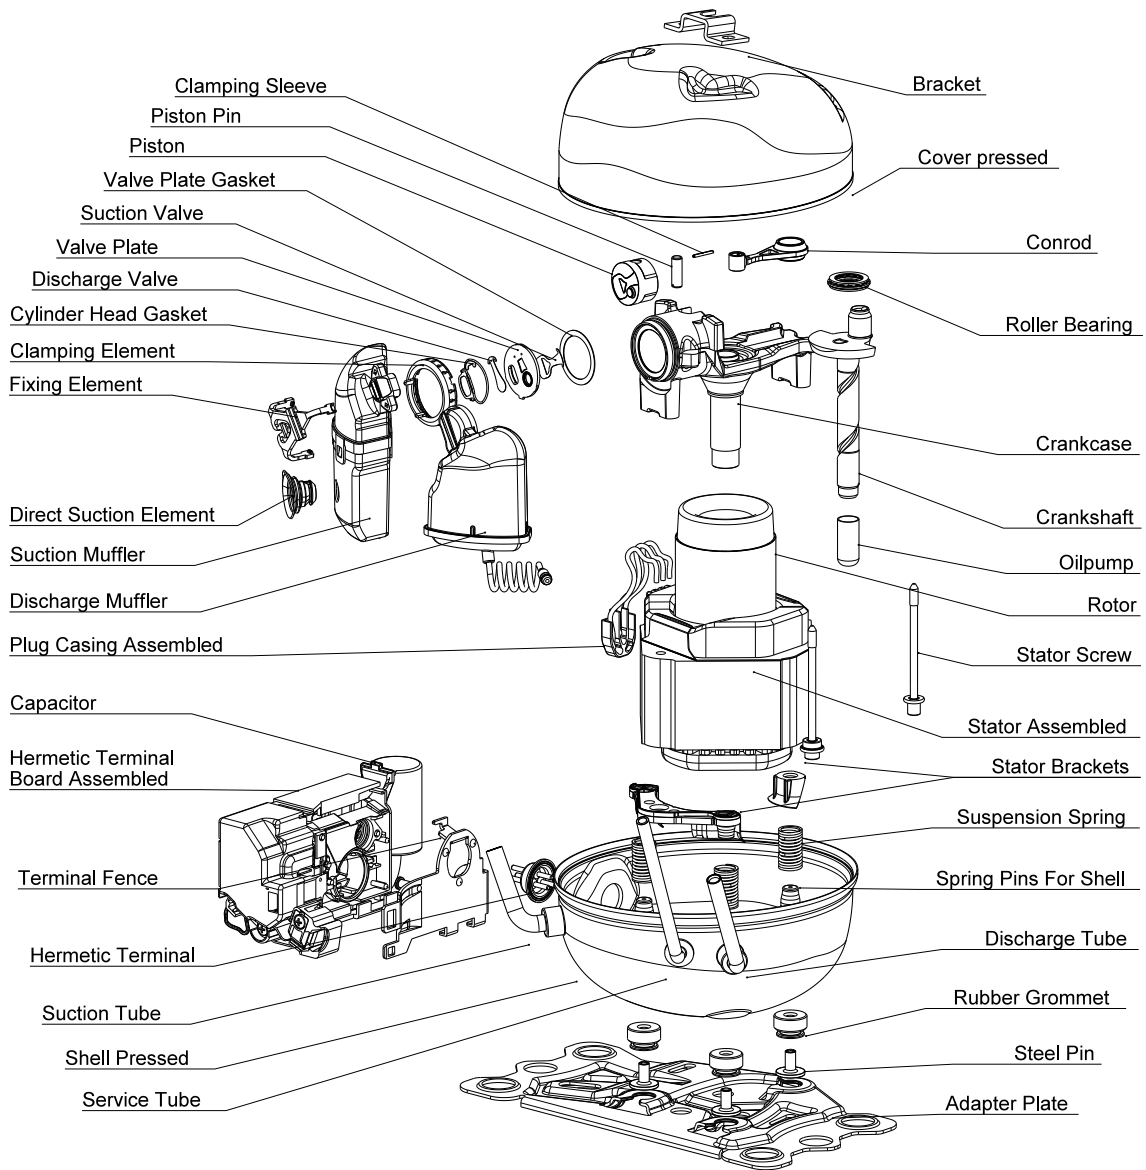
Explosionszeichnung des Delta Kompressors inklusive Bauteilbenennungen
